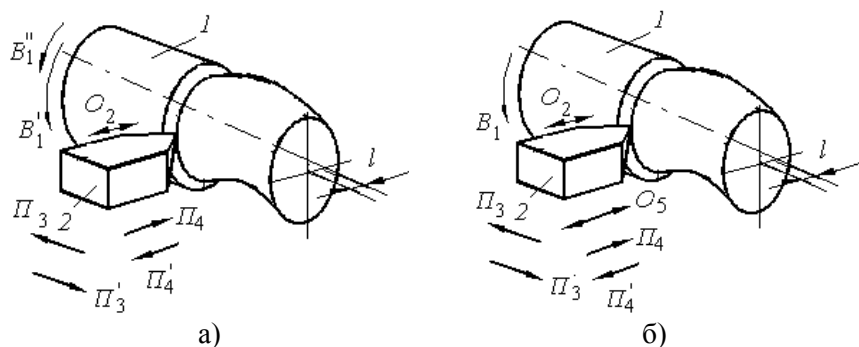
Схемы точения КВП при сообщении дополнительного движения заготовке (а) или резцу (б)
